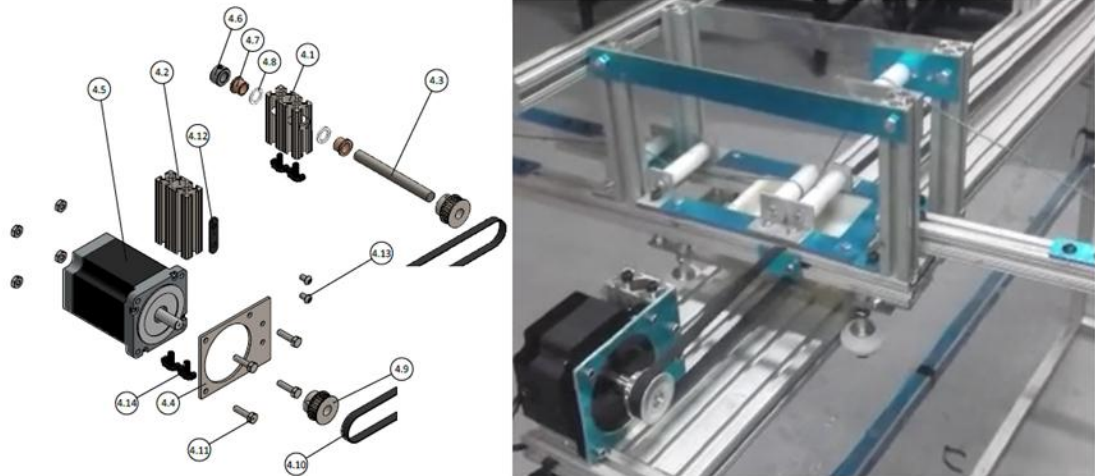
Procedimiento para el ensamble de la perfilería tipo hepco.
